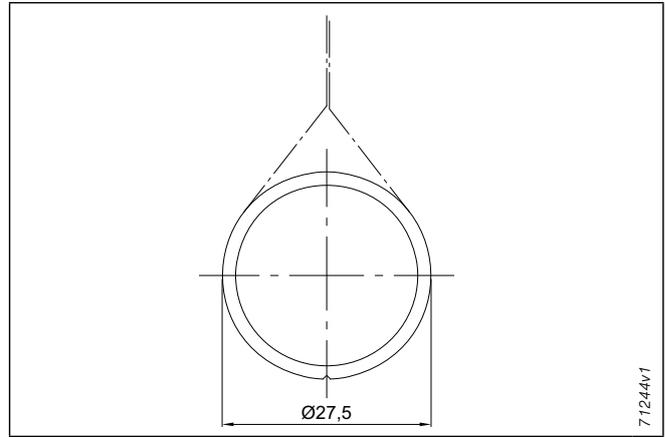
Fallprofil rund, klein, stoffumschlungen
